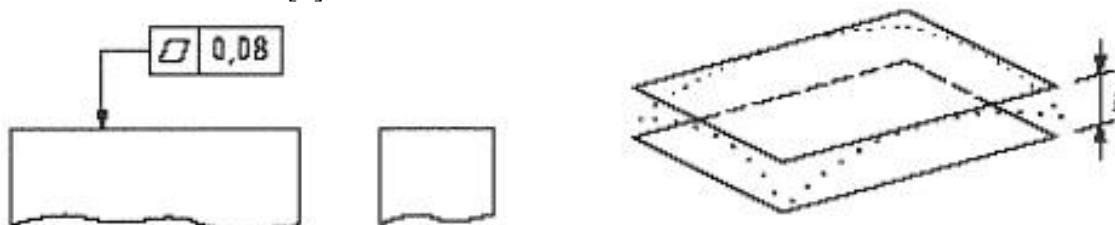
Označení a vysvětlení geometrické tolerance přímosti [4]
